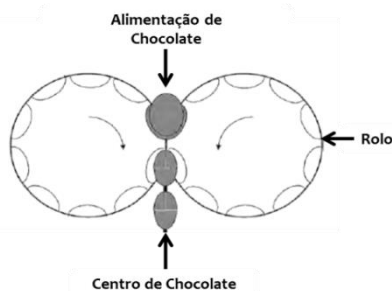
Processo de moldação de Centros (Beckett, 2008)
